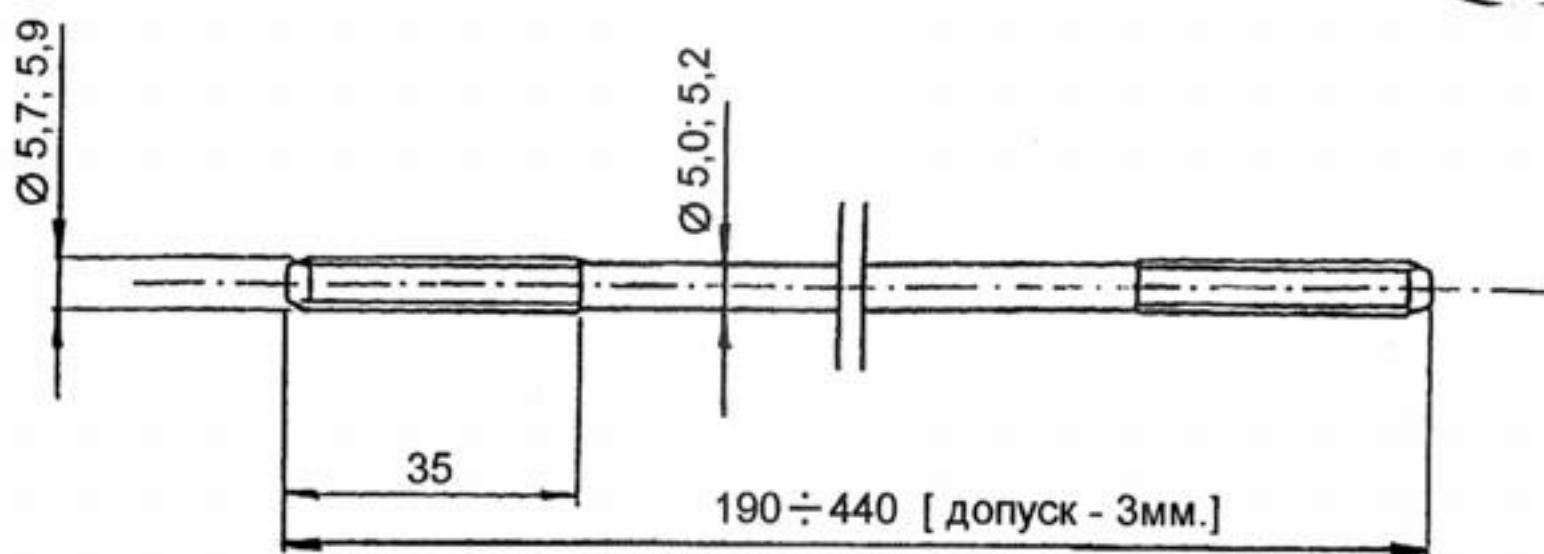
Стяжка с резьбовым внутренним креплением
